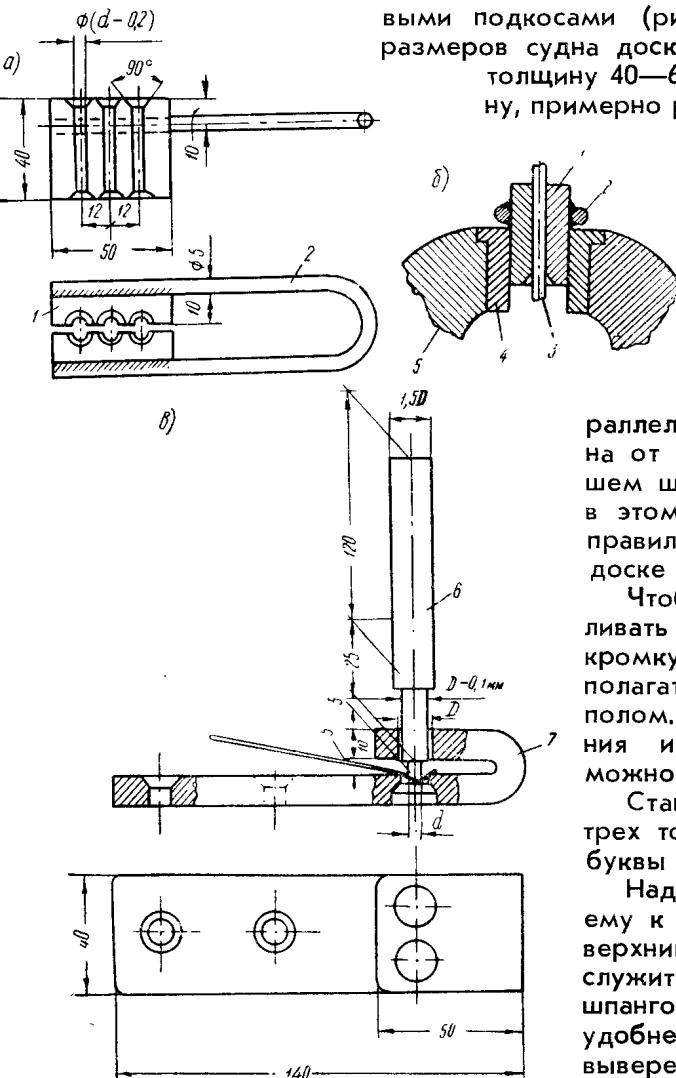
Приспособления для изготовления заклепок и шайб: а — приспособление для изготовления заклепок (гвоздильня); б — гвоздильня, закрепленная в тисках; в — ручной штамп для изготовления шайб.
